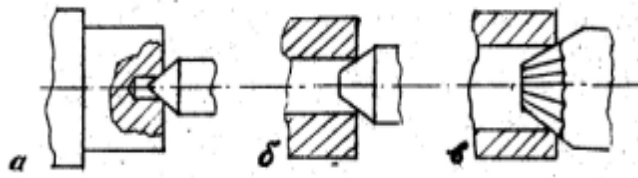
Схема базування оброблюваних деталей на центрових отворах
